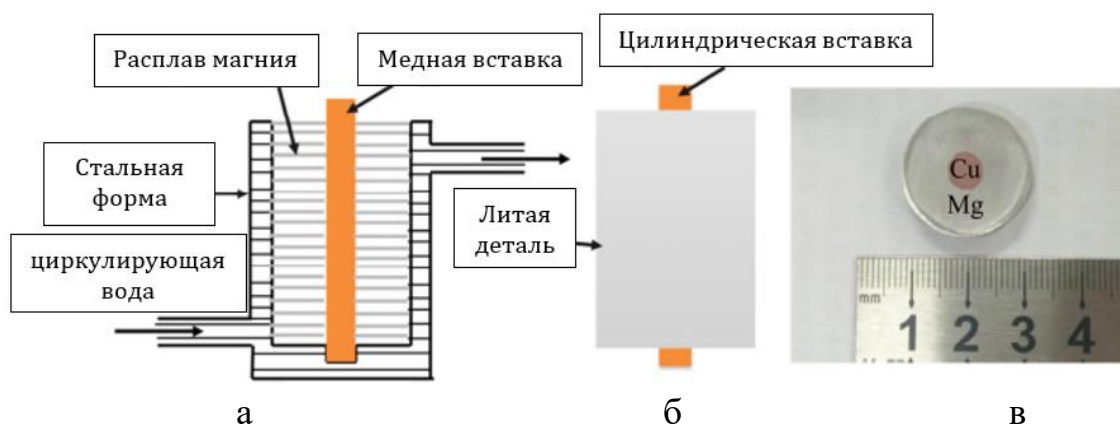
Схема изготовления Cu/Mg-композита методом литья (а), внешний вид биметаллической пары (б) и фото поперечного сечения образца (в) [104]
